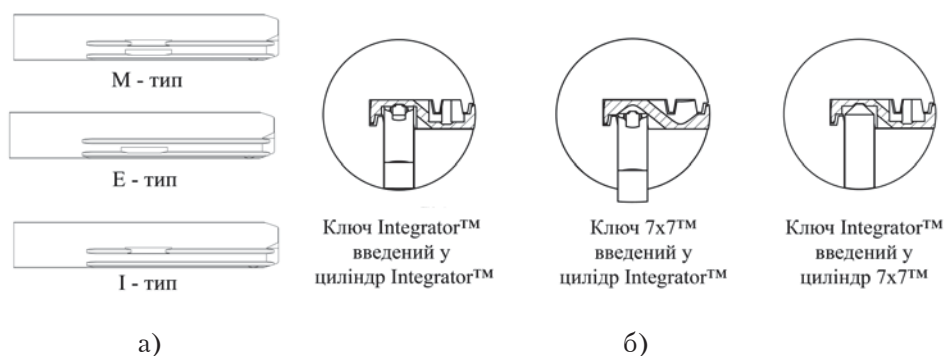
Варіанти заготовки ключа Integrator™ та принцип уніфікації з механізмами 7x7® (а – типи заглибин Integrator™; б – взаємозамінність ключів 7x7® й Integrator™)
